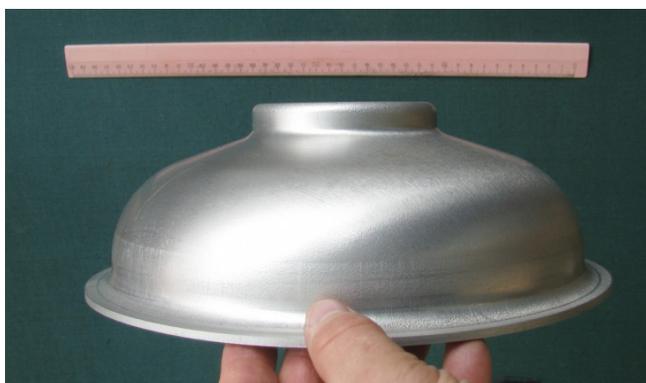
Внешний вид деталей типа «полукамера» - являющихся составными частями резонатора ускорителя электронов, изготовленных из особо чистого ниобия в ФТИ импульсной гидроударной штамповкой
